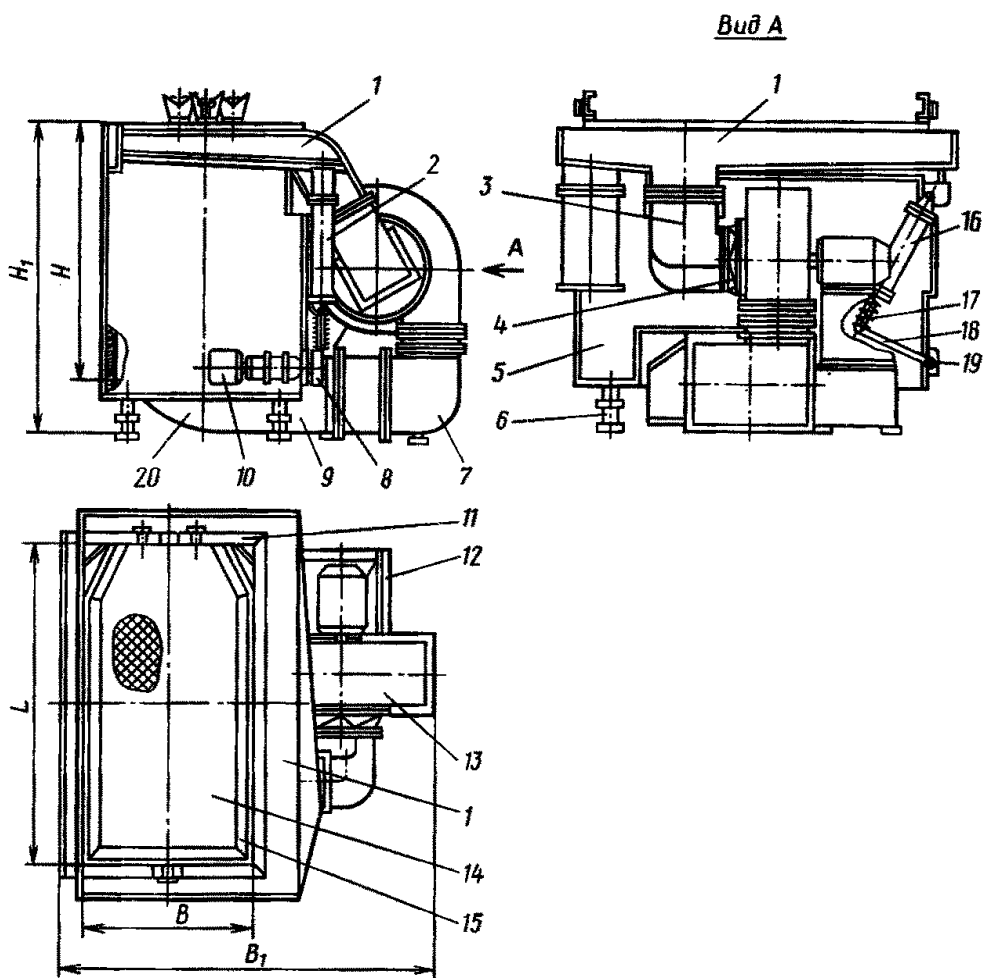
Камера для сушки деталей насыпью: 1,3 — вытяжные воздуховоды; 2 — патрубок; 4 — брезентовая вставка; 5 — корпус камеры; 6 — регулируемая опора; 7, 20 — нагнетающие воздуховоды; 8 — кожух клиноременной передачи; 9 — электрокалорифер; 10 — мотор-редуктор; 11 — опоры с подводом питания к электродвигателю барабана; 12 — рама вентиляторного агрегата; 13 — вентиляторный агрегат; 14 — сетчатое дно; 15 — подвижная рама; 16 — пневмоцилиндр; 17 — пружина; 18 — рычаг; 19 — ось.
